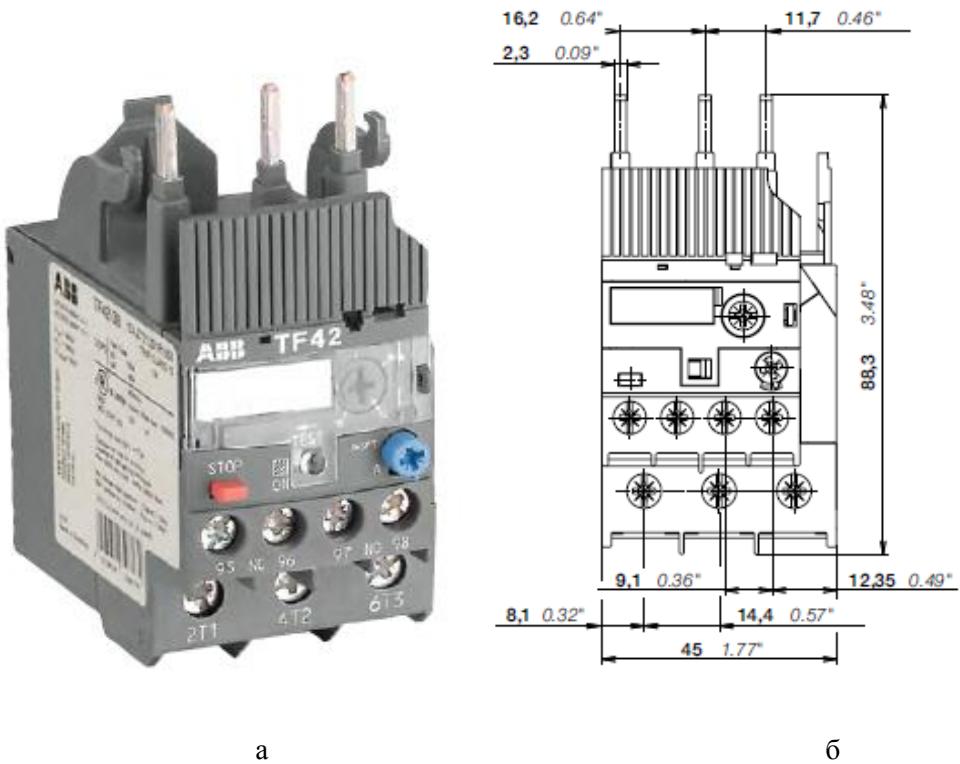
Общий вид (а) и габаритные размеры (б) теплового реле TF-42-24.
